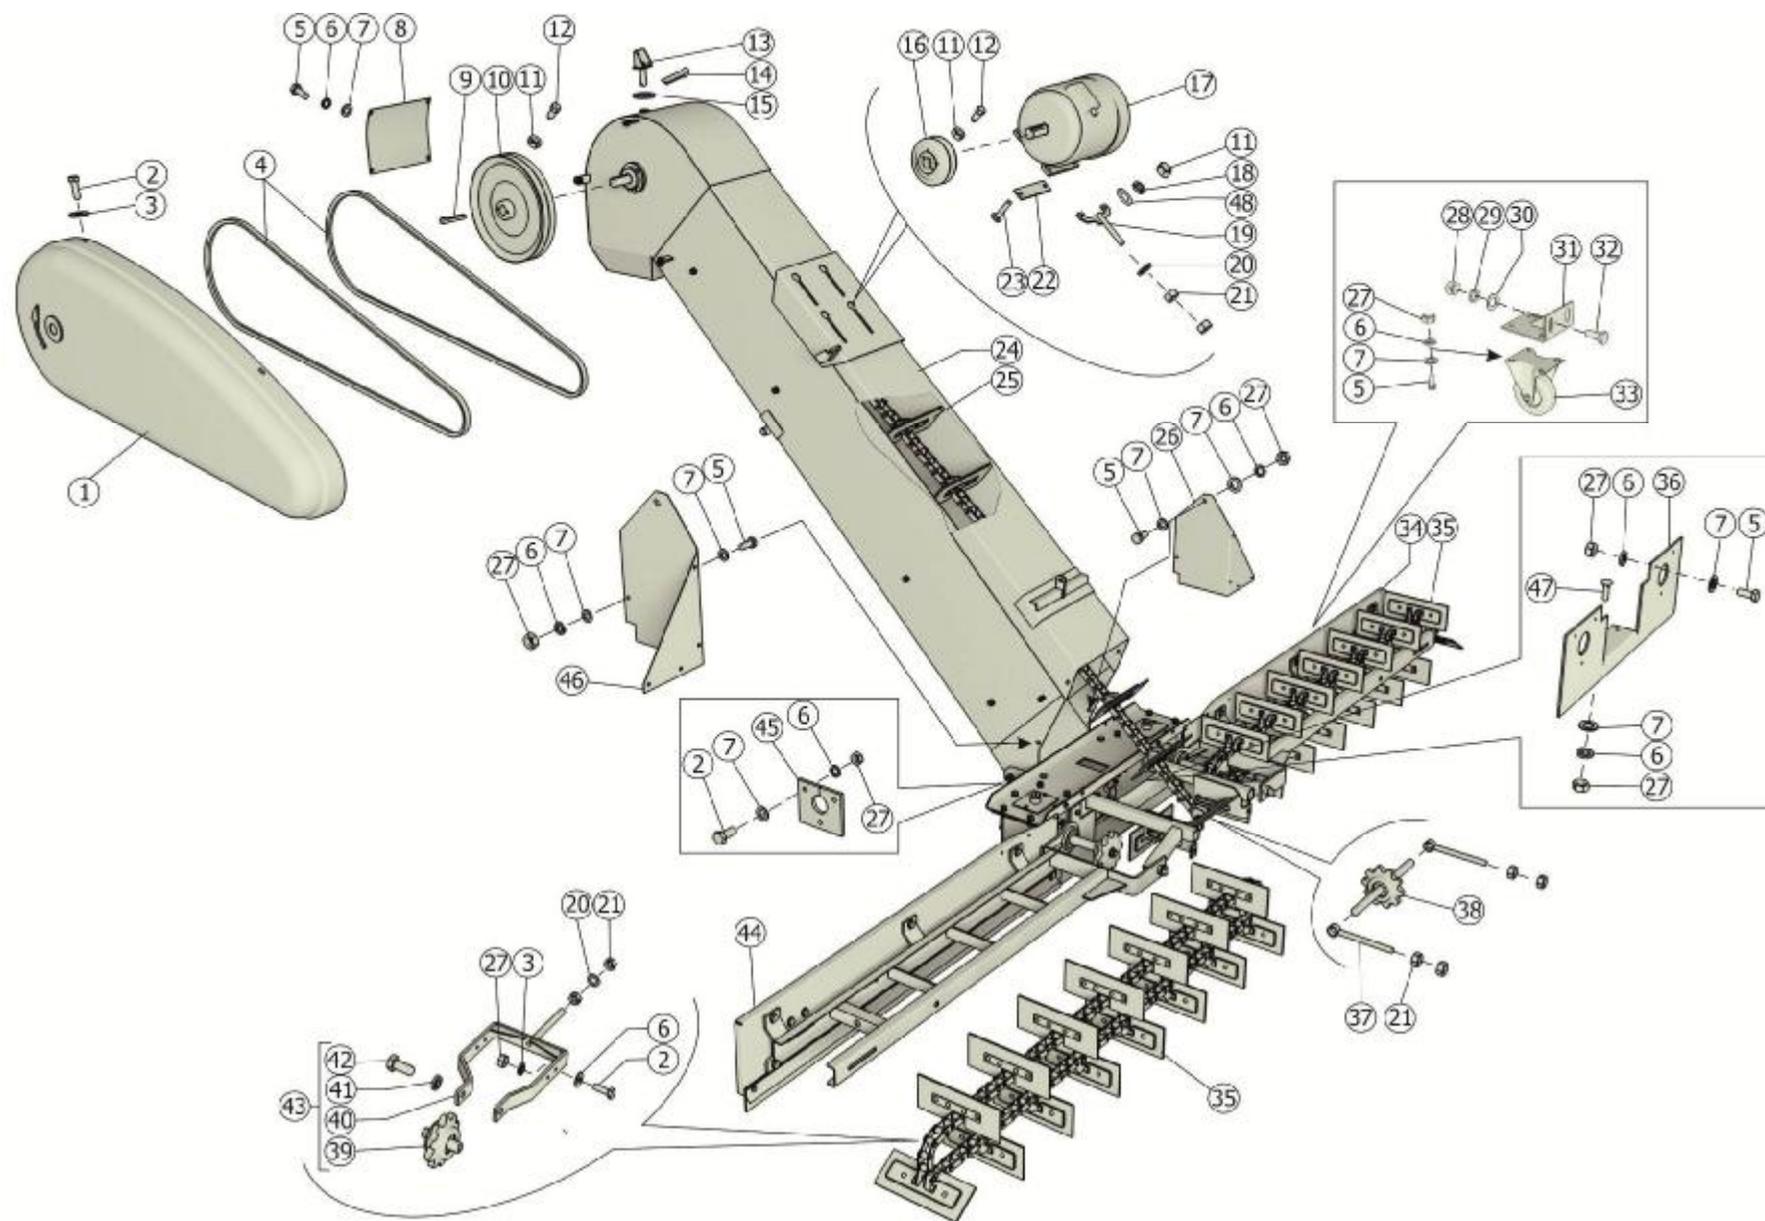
Транспортер загрузочный МЗС-90.03.000
